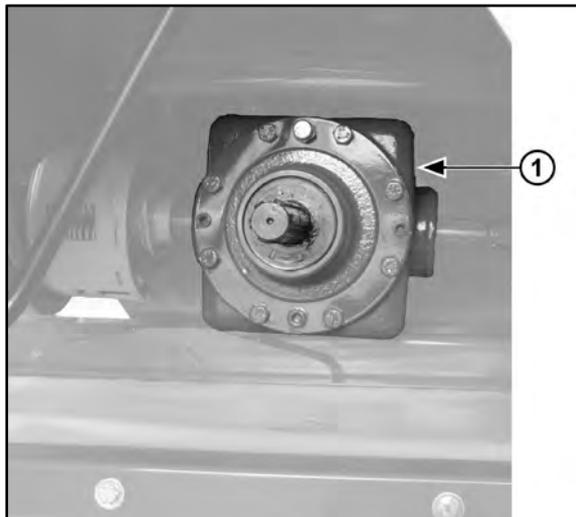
Tornillo de inspección del nivel de aceite de la caja de engranajes rectos
